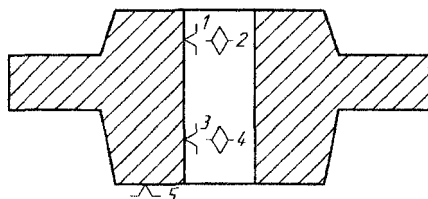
Схема базирования заготовки колеса для зубофрезерования на разжимную оправку при коротком отверстии и торце большого диаметра
